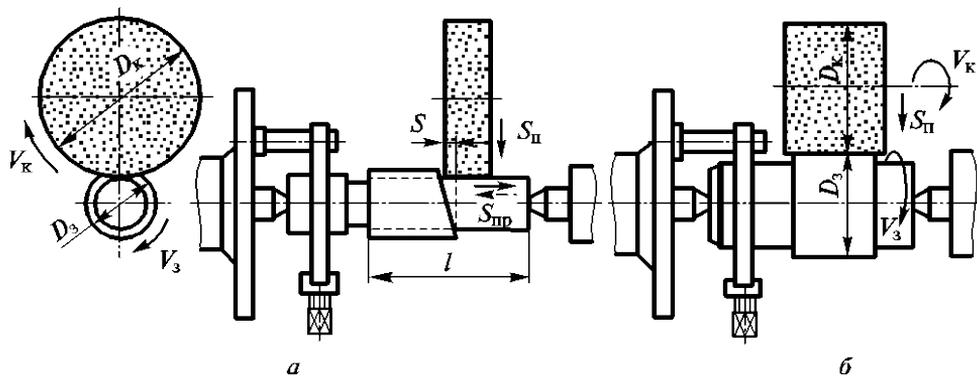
Схемы наружного круглого шлифования с продольной (а) и поперечной (б) подачей инструмента
